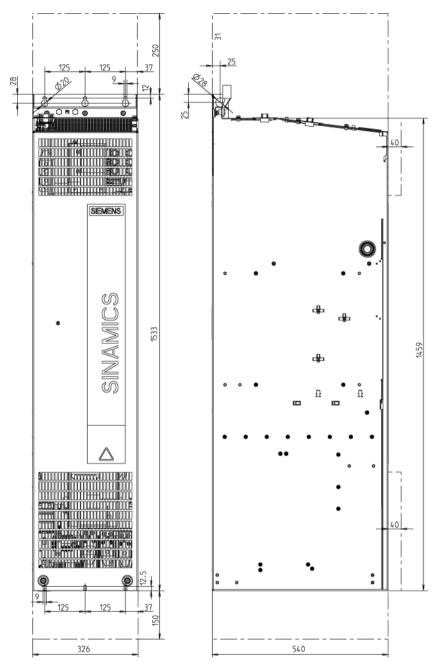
Габаритный чертеж активного модуля питания, типоразмер GX. Вид спереди, вид сбоку
